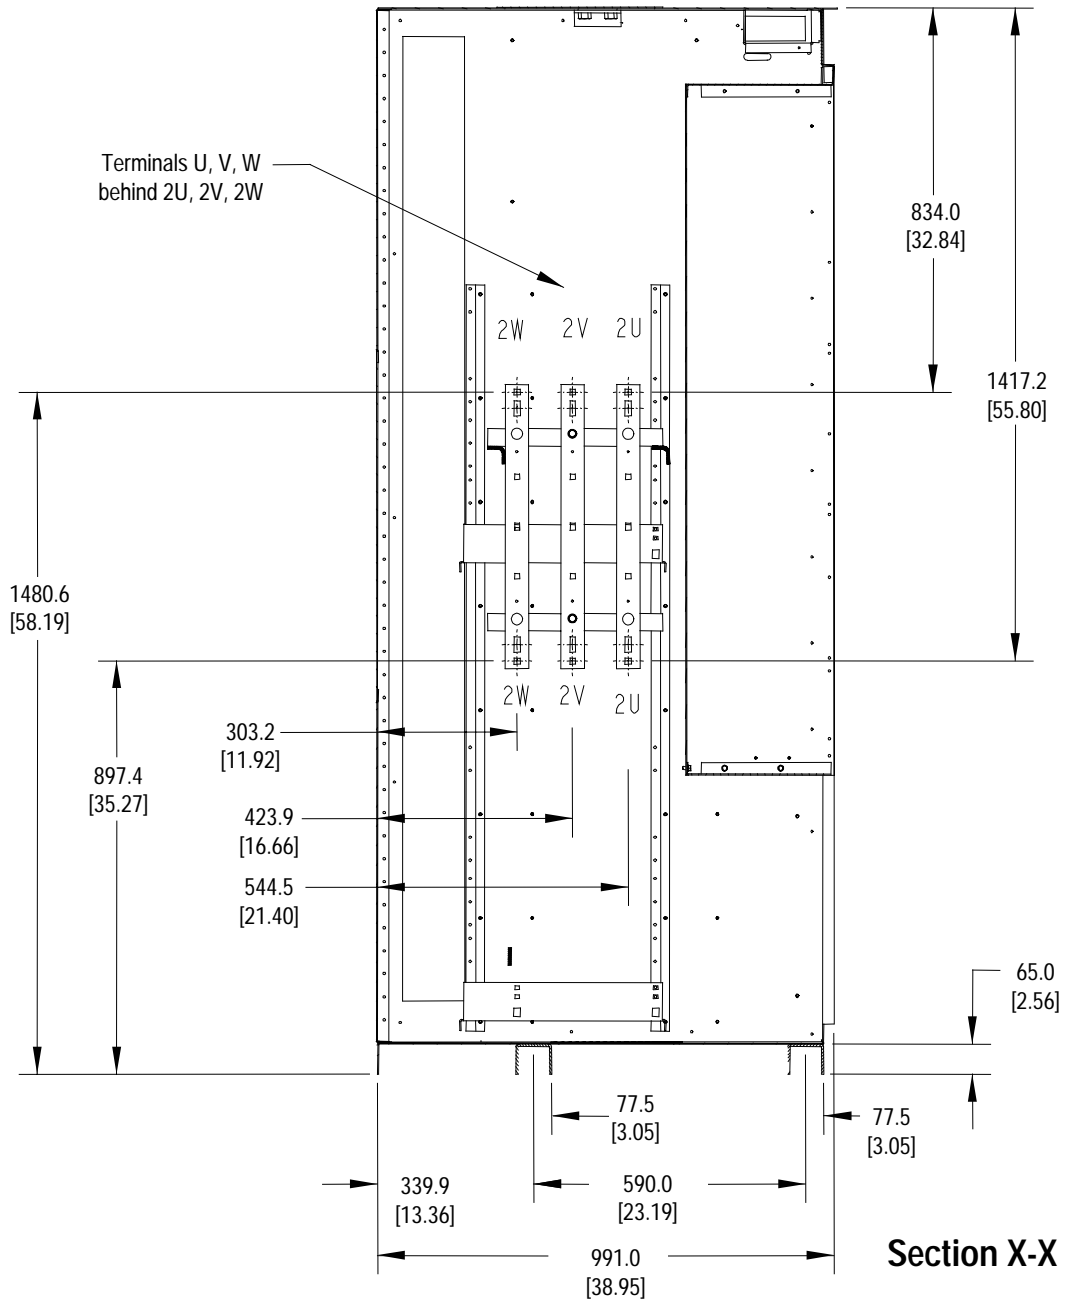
Detaillierte Abmessungen der Versorgungsanschlüsse
